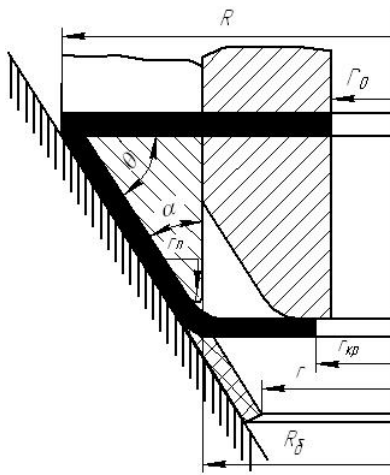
Схема процесса формовки и отбортовки:
